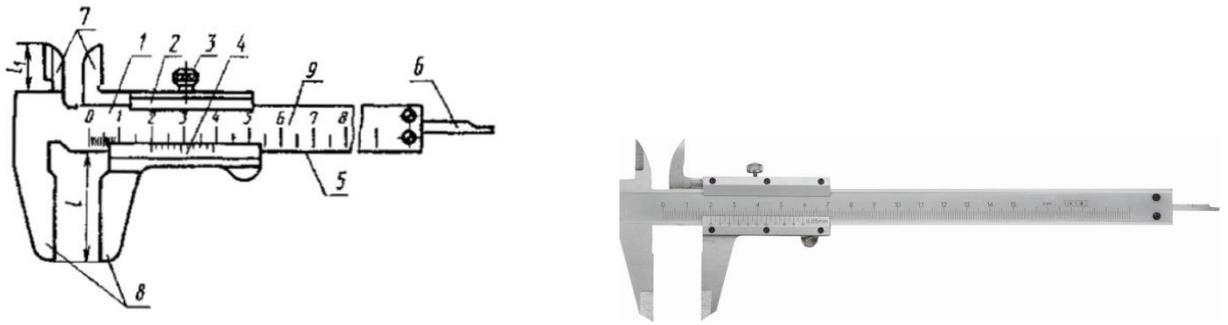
Двусторонний штангенциркуль типа ШЦ-I
